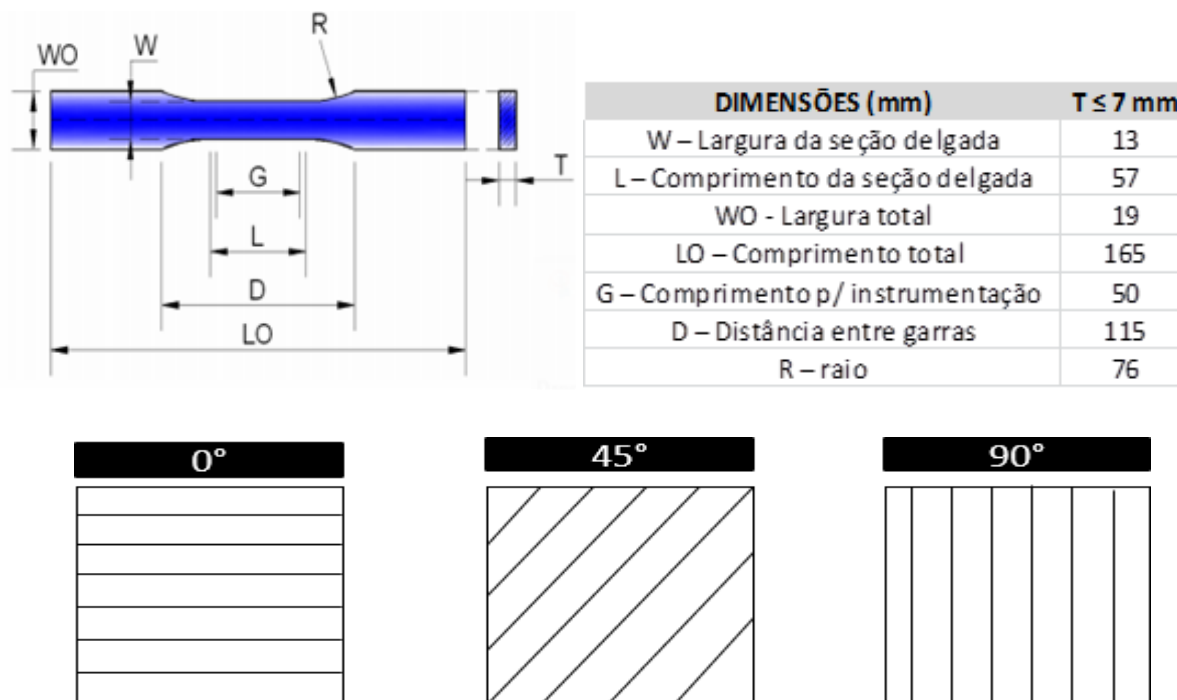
Corpo de prova com dimensões padronizadas e representação das direções de corte.
